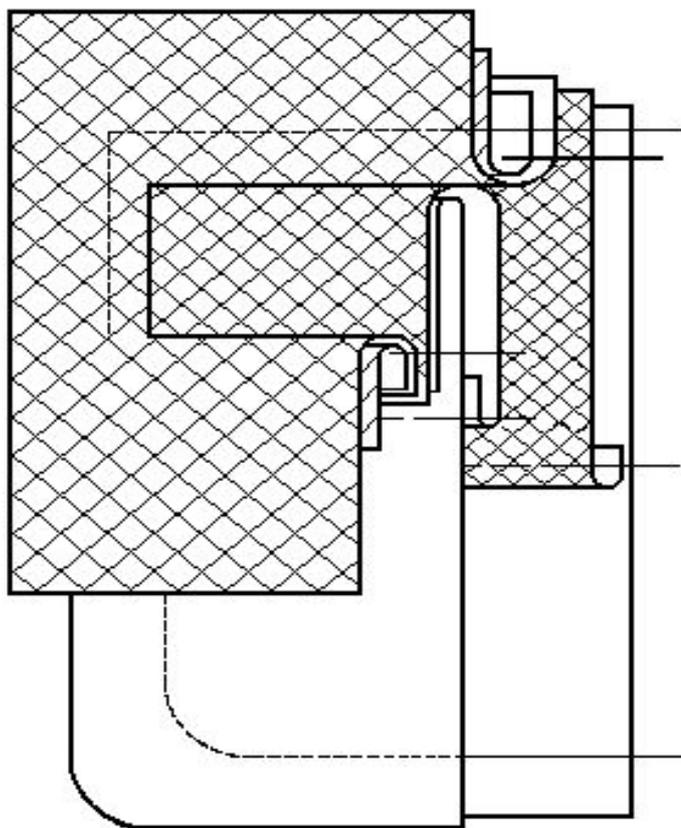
Схема метода поузловой обработки внутреннего кармана с листочкой из подкладочной ткани на полочках подкладки
